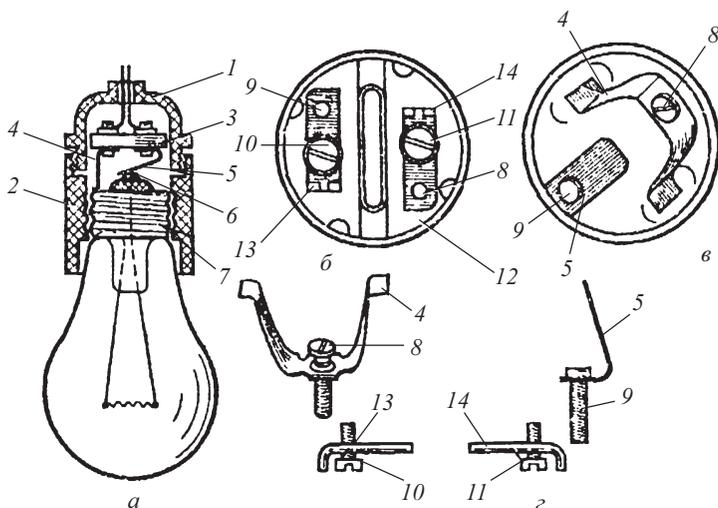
Устройство резьбового патрона для ламп накаливания с цоколем E27
